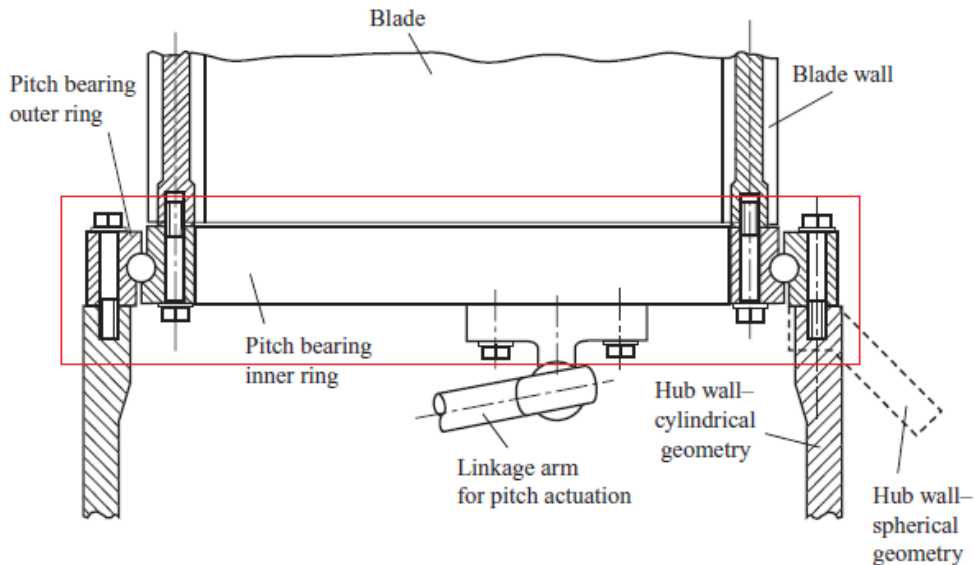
Esquema de montaje del rodamiento de “pitch”.
